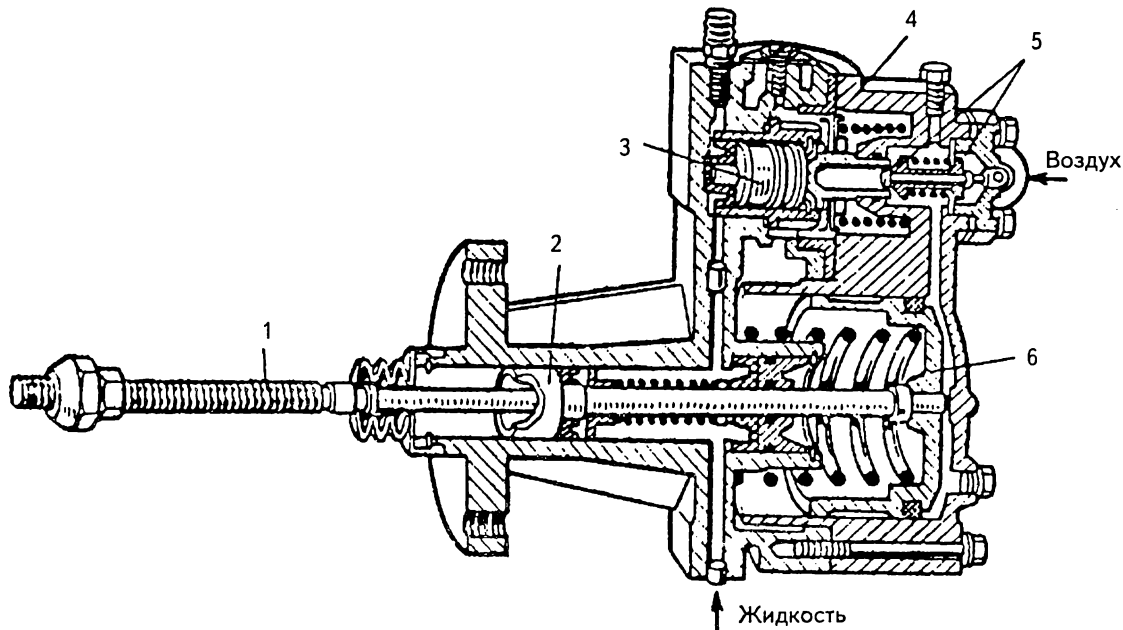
Пневмоусилитель гидравлического привода механизма выключения сцепления:
